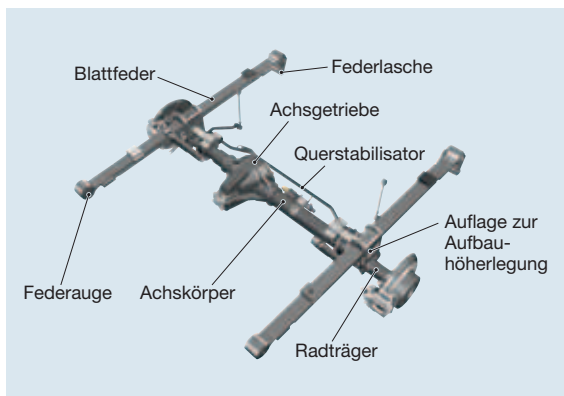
Starrachse für leichte Nutzfahrzeuge
